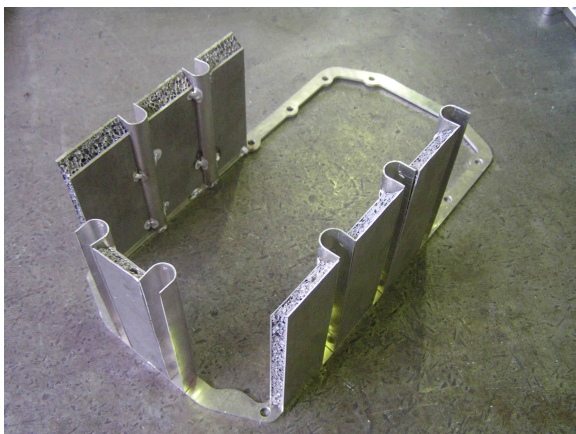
Gerade Wandelemente mit Flansch verschweißt
